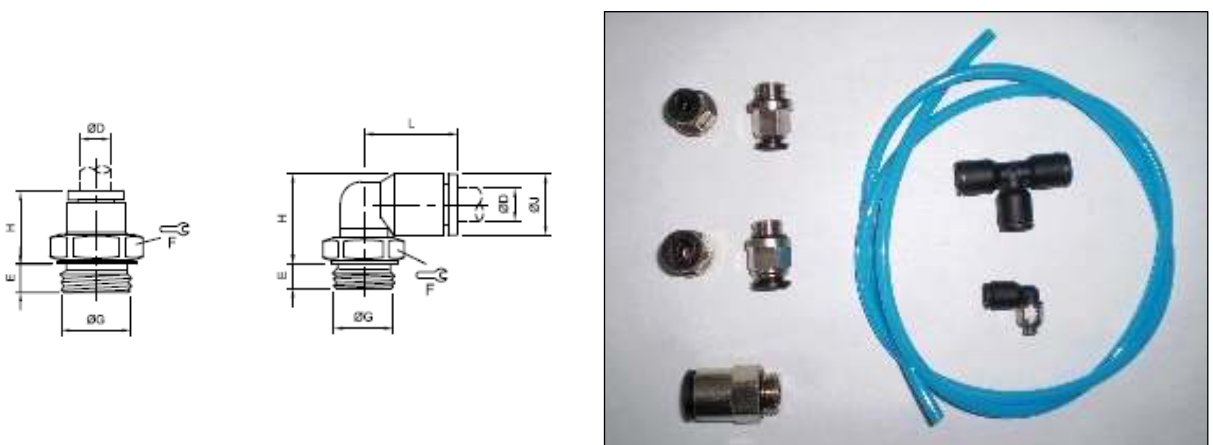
Detalles de las conexiones entre elementos de la cámara.
